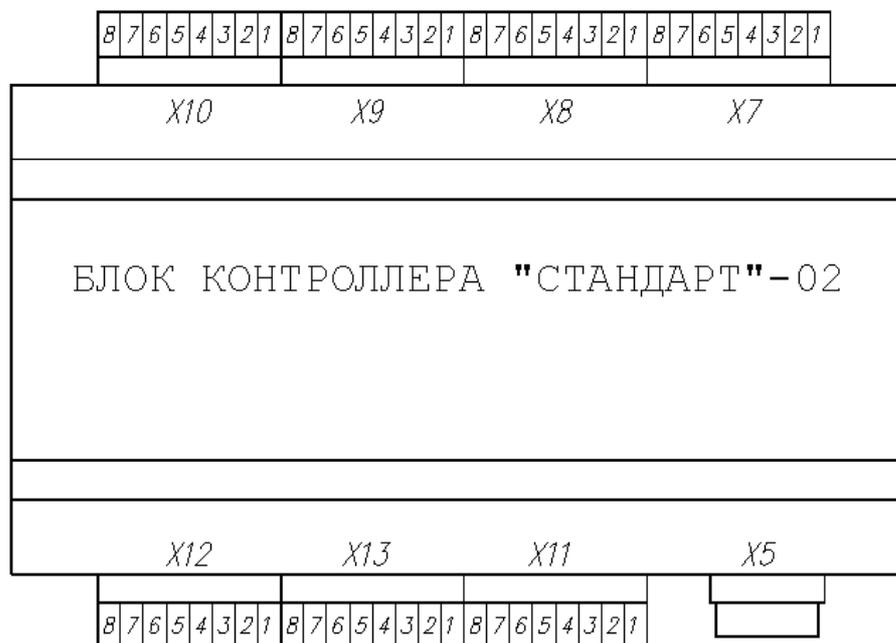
Внешний вид блока контроллера «Стандарт»-02
